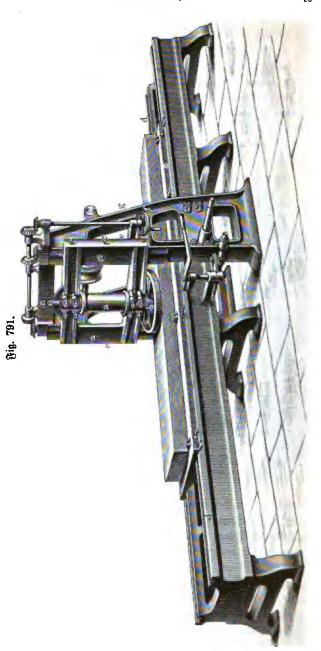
Die Messer ragen aus ber unteren Fläche ber auf ber senkrechten Spindel a befestigten Scheibe b hervor, die durch einen auf a gestührten halbgeschränkten Riemen schnell umgedreht wird, während das zu hobelnde Holz auf der Tischplatte c durch geeignete Spannvorrichtungen besestigt ist. Wenn diese in den prismatischen Führungen des Bettes d geleitete Tischplatte in der von den Metallhobelmaschinen her bekannten, in der Figur nicht näher erläuterten Art langsam verschoben wird, so wird durch die Resser oder stichelsörmigen Schneiden der Scheibe d die obere Fläche des Holzes in der schon oben besprochenen Weise abgerichtet. Die Messer welle sindet hierbei ihre Lager in einem Rahmen e, der an den senkrechten Führungsbahnen des Gestelles g vermittelst der beiberseits angebrachten Schraubenspindeln durch Umdrehung des Handrades f sehr genau verstellt werden kann, so daß man hierdurch nicht nur die Stärke des abzunehmenden Spanes in der Hand hat, sondern auch den seweiligen Dicken verschiedener Hölzer entsprechend die Stellung der Messerschiebe bestimmen kann.
